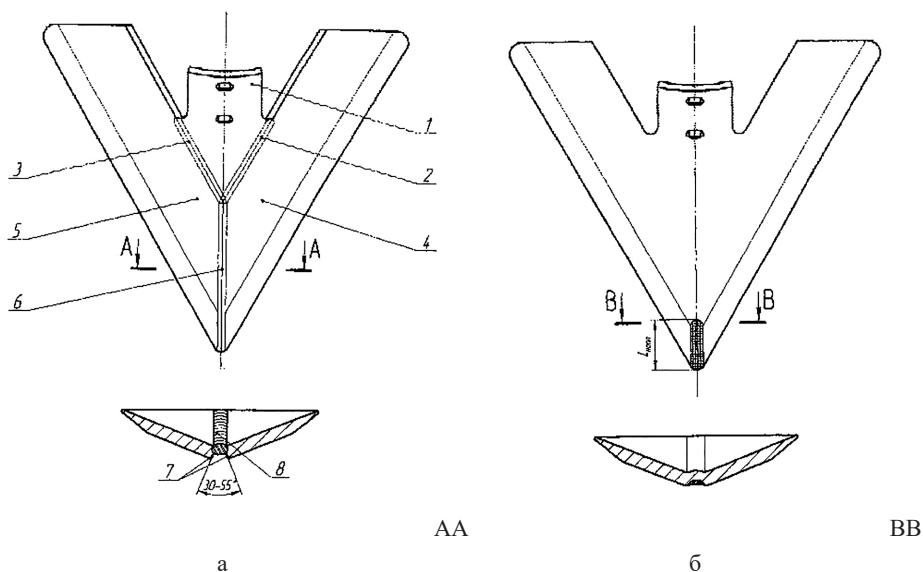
Схема наплавки носовой части сварной (а) и штампованной лапы (б)
